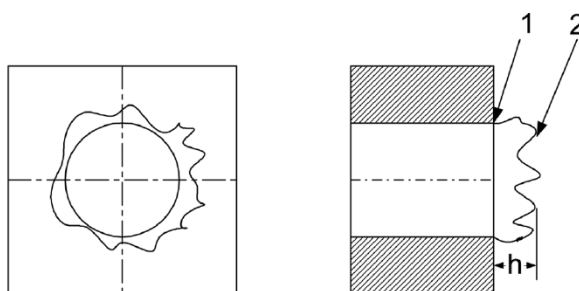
Průběh vzniku otřepu ve formě kloboučku [10].
